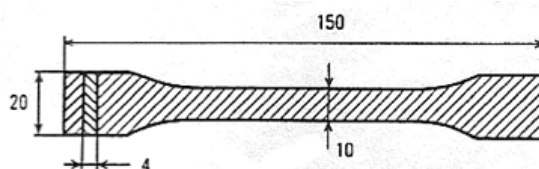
Универсальный образец для испытаний ISO R527 [1]
